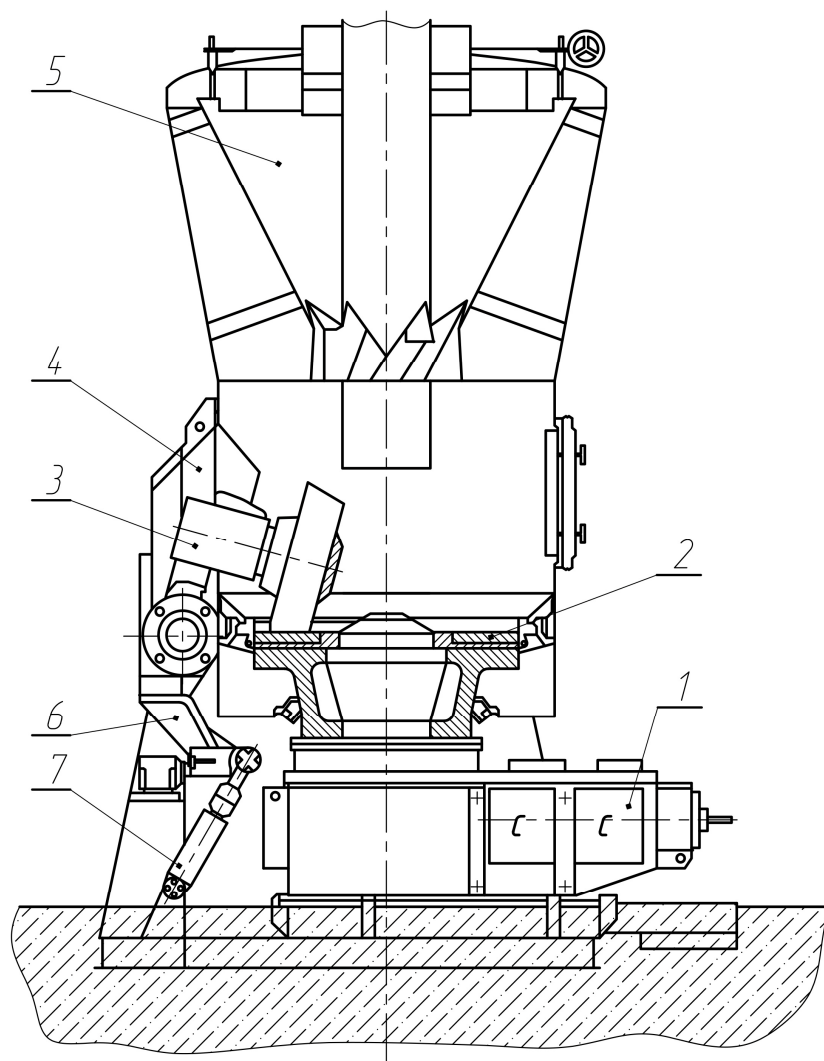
Конструкция валково-тарельчатой мельницы: 1 — привод вращения стола; 2 — размольный стол; 3 — узел размольного конического валка; 4 — крышка валка; 5 — сепаратор; 6 — рычажный узел; 7 — гидроцилиндр прижима валка к столу
